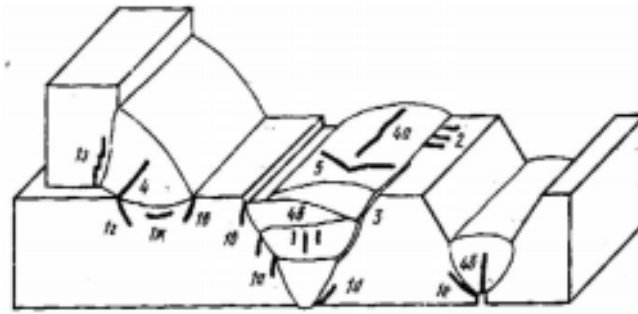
Різновиди холодних тріщин, що відрізняються зовнішнім виглядом та місцем розташування в зварному з'єднанні [9]:
